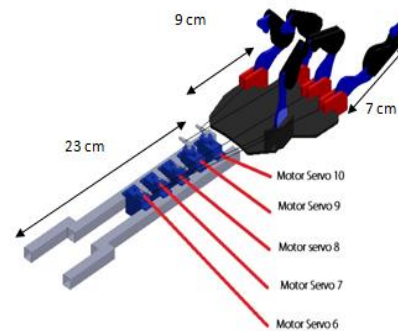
Dimensi Lengan Robot Berjari dan Posisi Motor Servo
